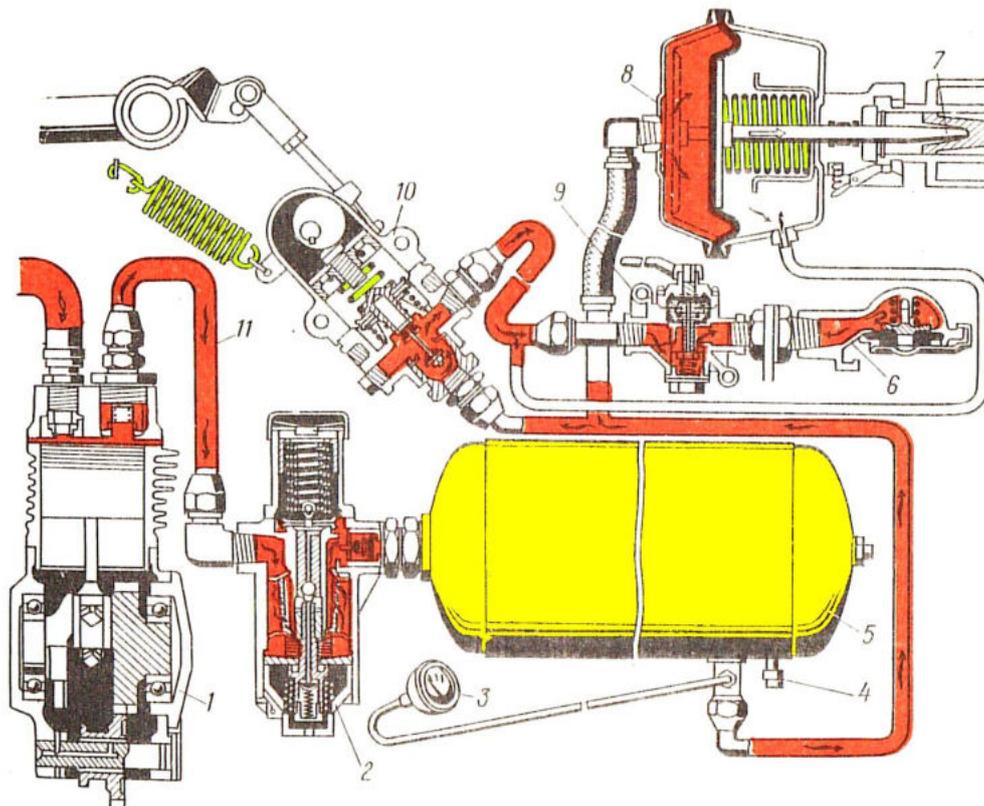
Схема пневматической системы привода тормозов прицепа трактора МТЗ-80:
